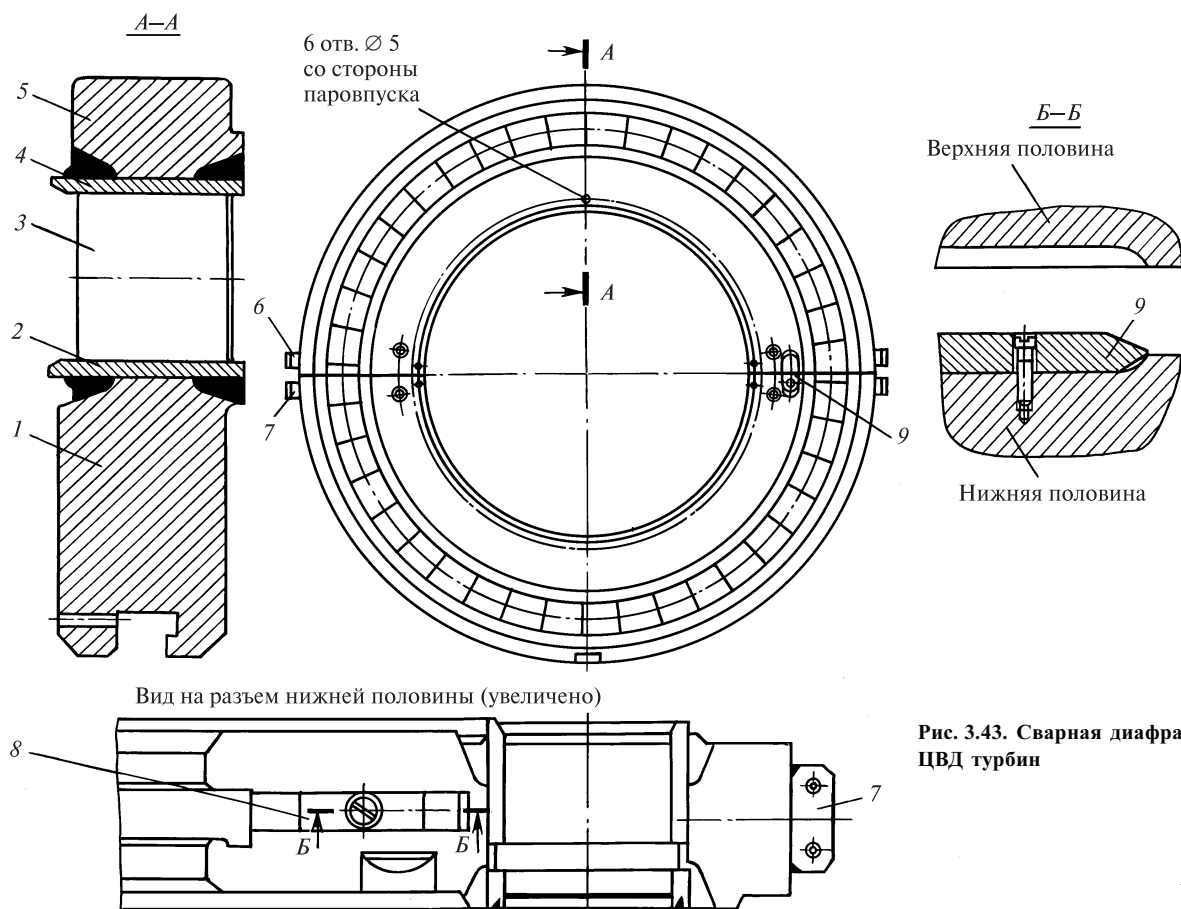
Сварная диафрагма для ЦВД турбин
